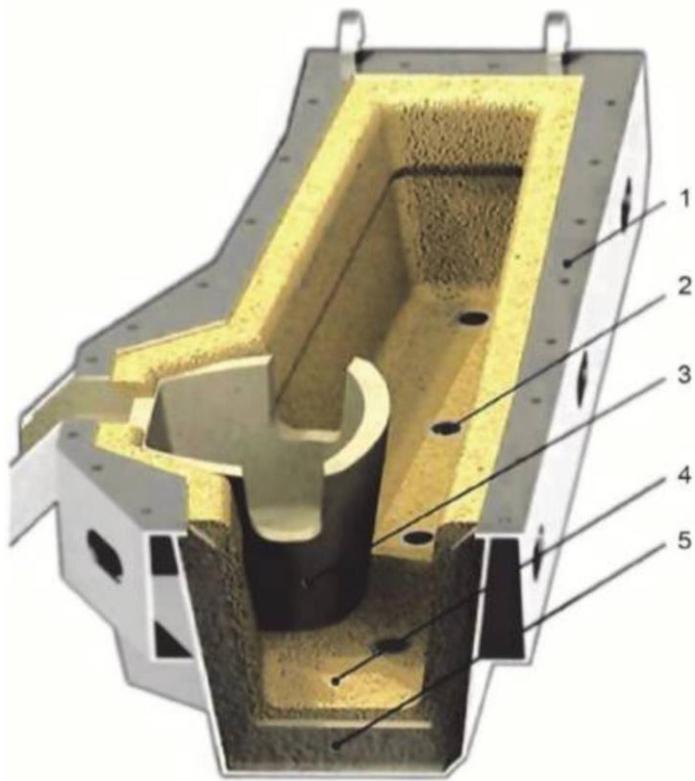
Вид сталеразливочного ковша в разрезе
